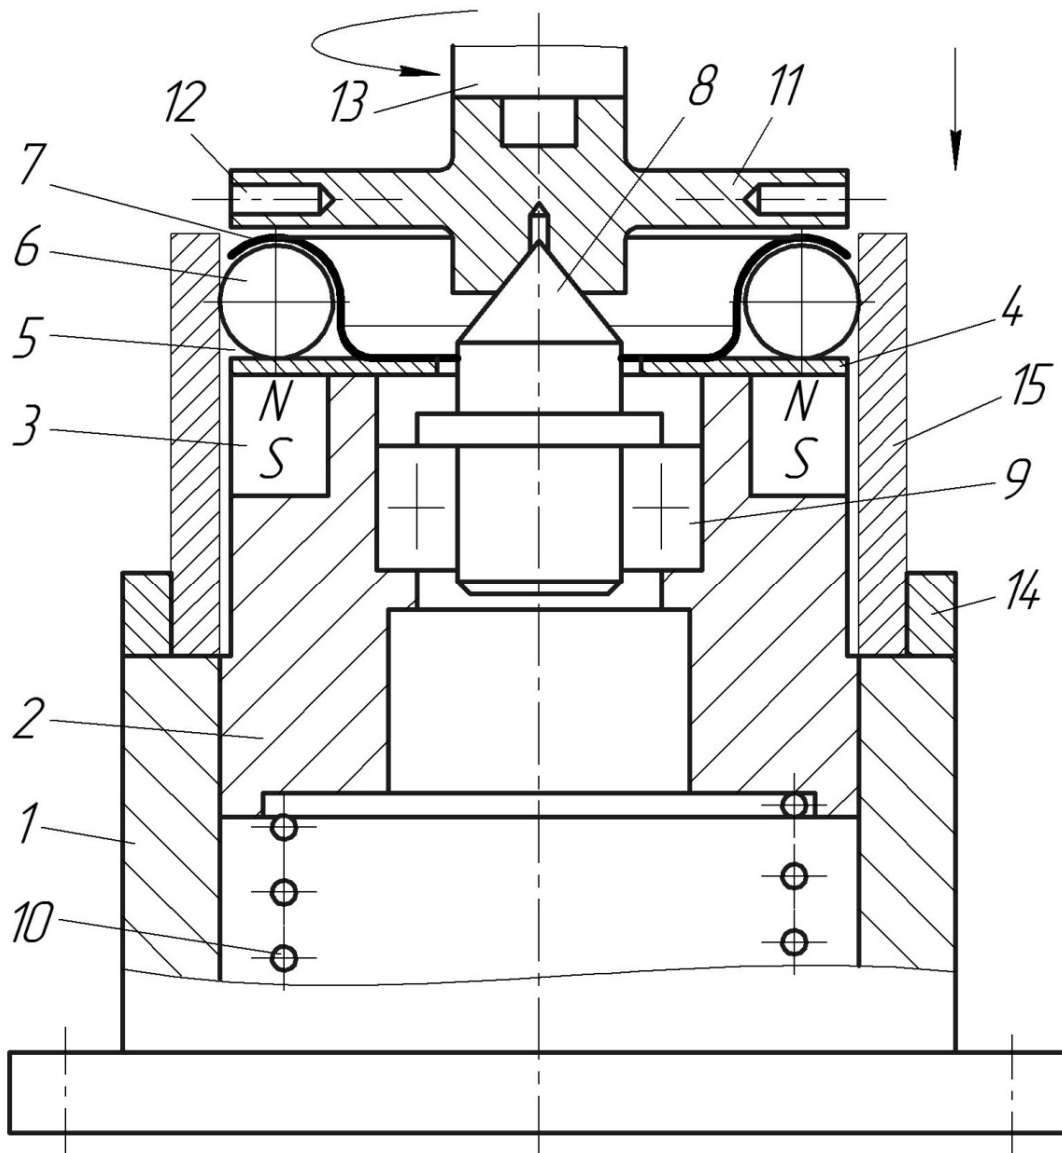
Схема инструмента с вращающимся магнитопроводом для совмещенной упрочняющей обработки внутренней поверхности цилиндров: 1 – цилиндрический корпус; 2 – шток; 3 – источник магнитного поля; 4 – шайба; 5 – кольцевая камера; 6 – деформирующие шары; 7 – кожух; 8 – вращающийся центр; 9 – подшипник; 10 – пружина; 11 – кольцевой магнитопровод; 12 – радиальные отверстия; 13 – оправка; 14 – упругое кольцо; 15 – упрочняемый цилиндр
